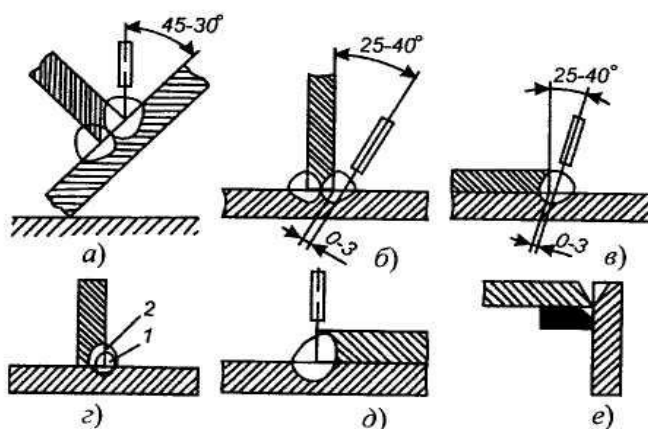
Автоматическая сварка под флюсом угловых швов
